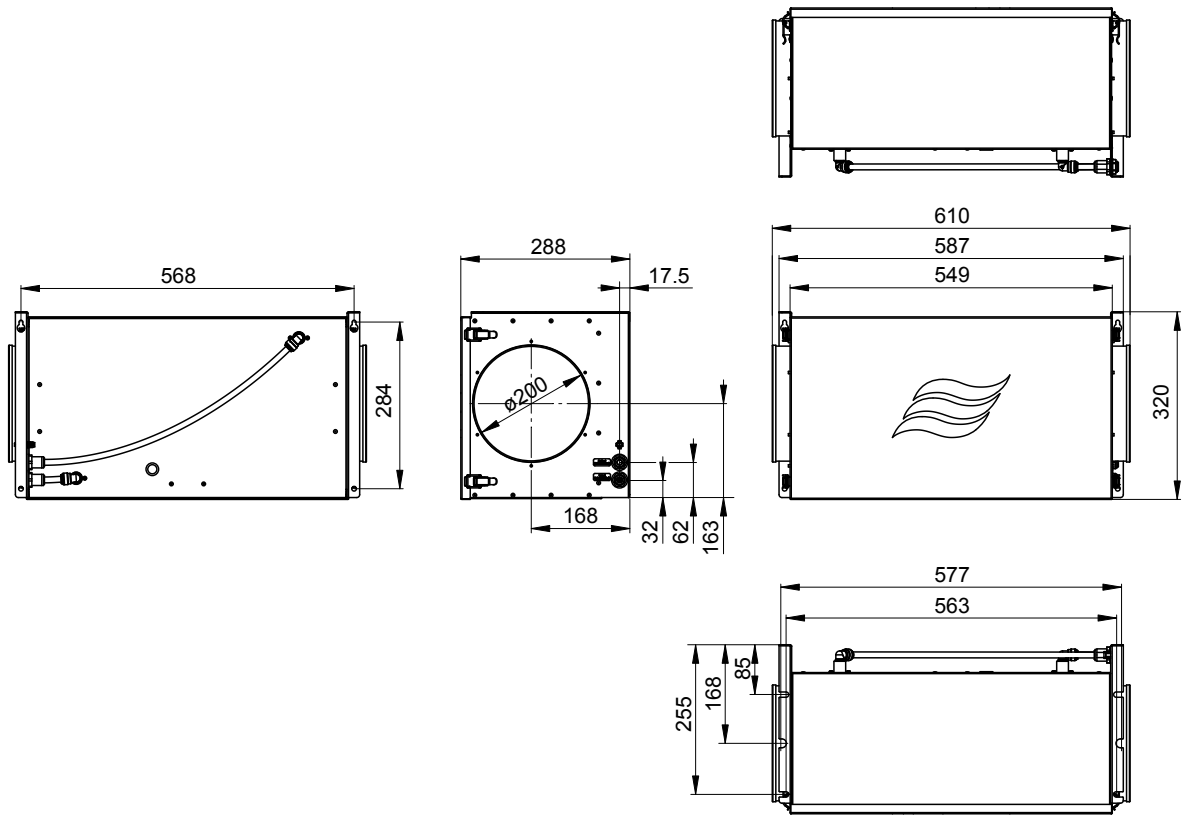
Dimensions unité d'humidification (dimensions en mm)
